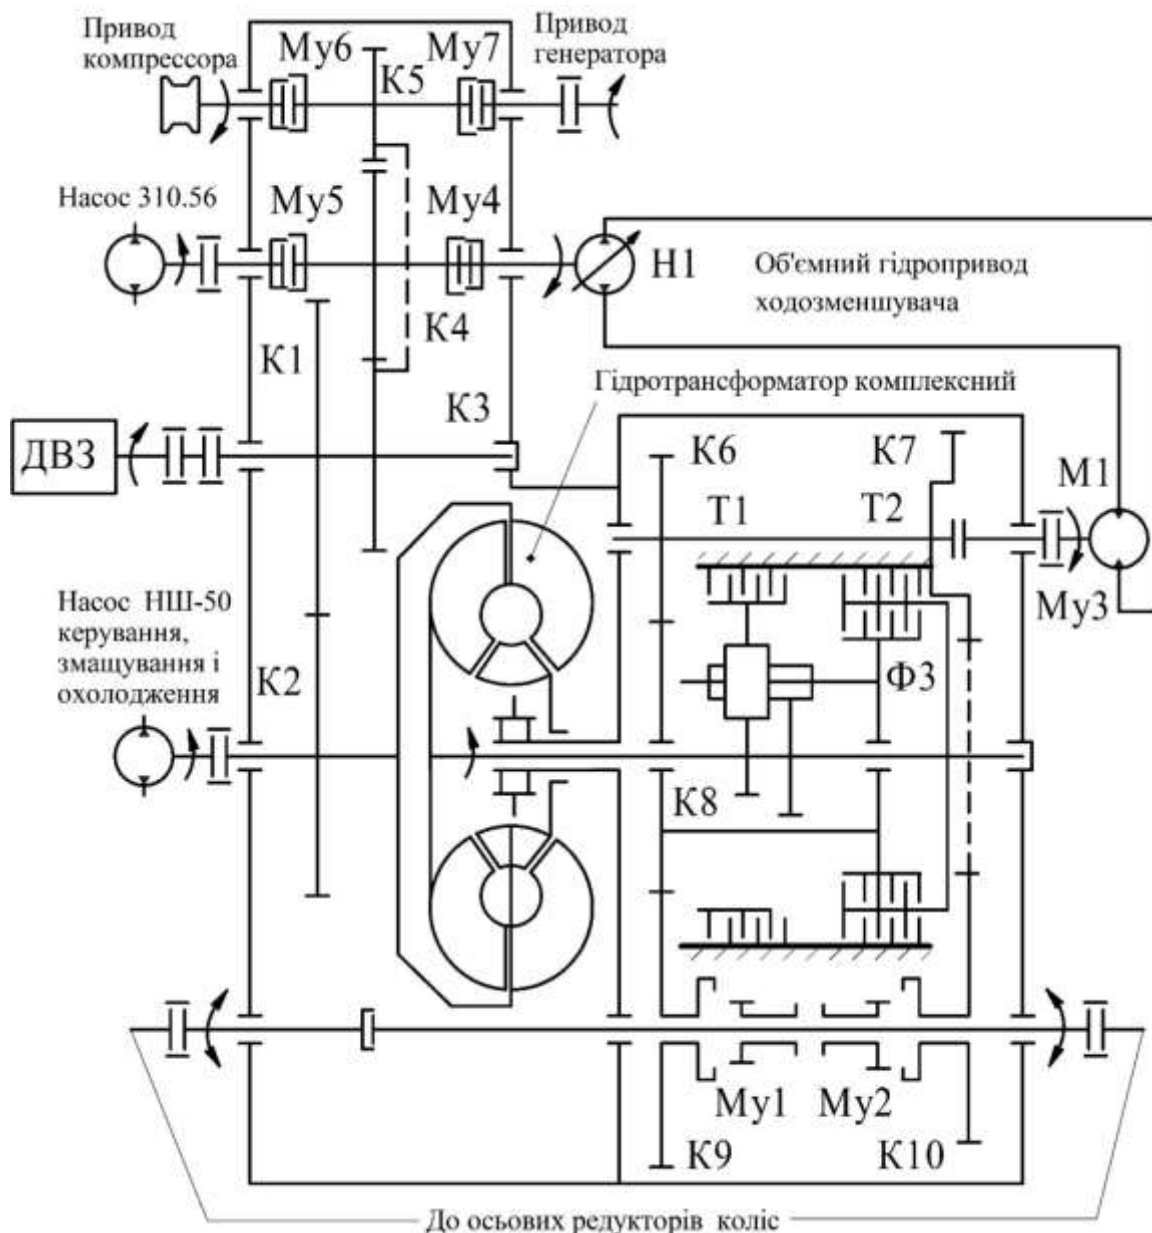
Схема гідромеханічної передачі ГП-300: К1...К10 – зубчасті колеса; My1...My7 – керовані зубчасті муфти; Т1, Т2 і Ф3 – фрикціони
